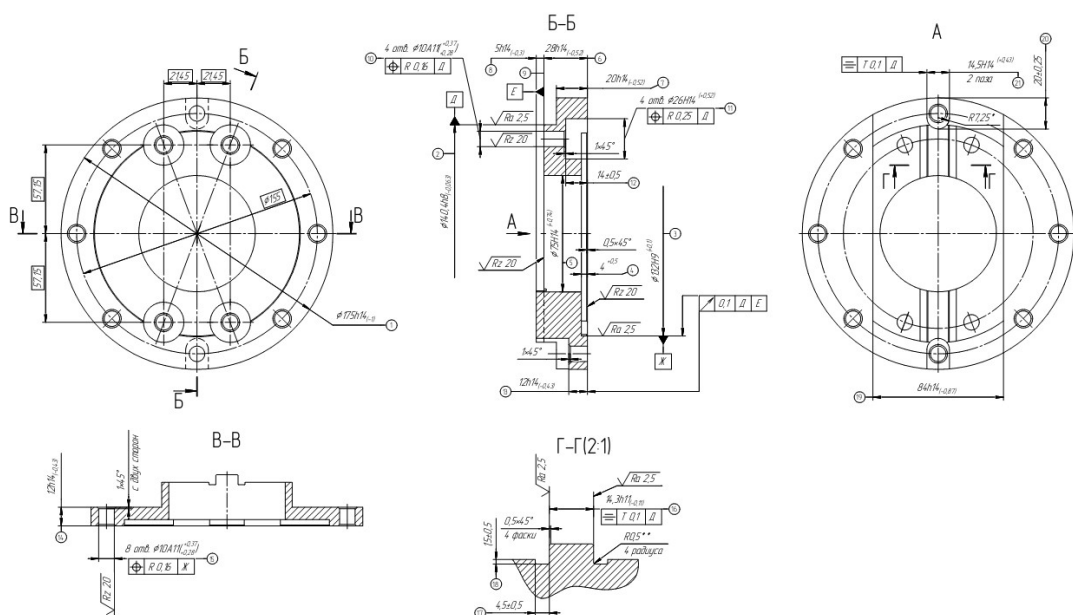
Ескіз деталі з позначеними поверхнями
